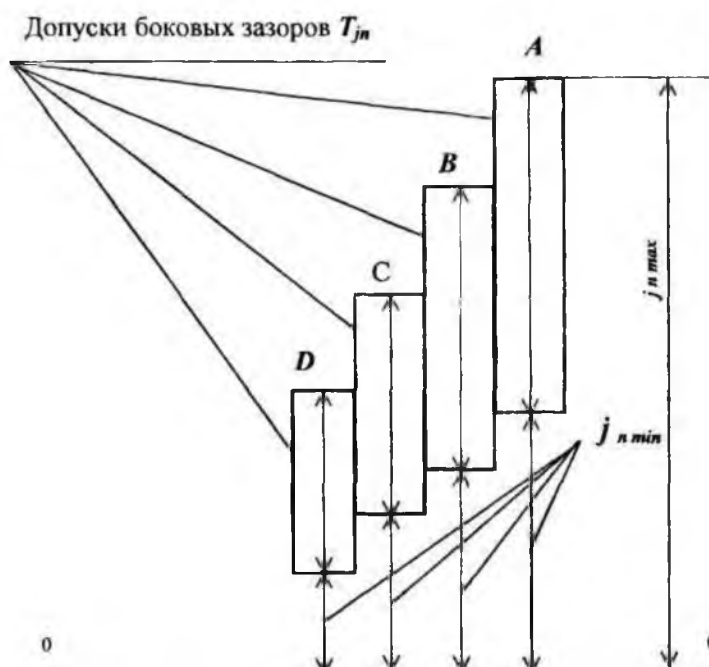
Виды сопряжений и величины боковых зазоров
